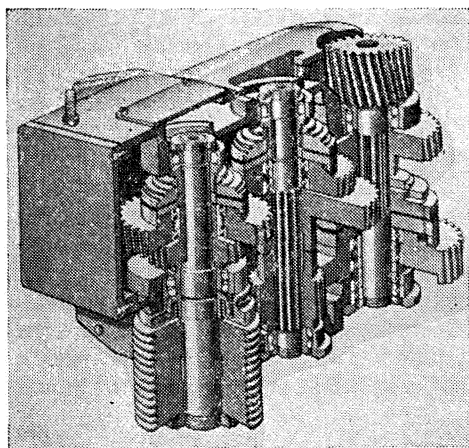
Схема трехступенчатой коробки перебора с электромагнитными зубчатыми муфтами
